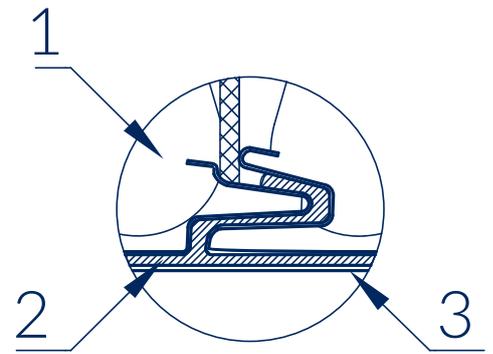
Соединение охлаждающей панели наружной стены с полом, холодильной морозильной камерой	70
